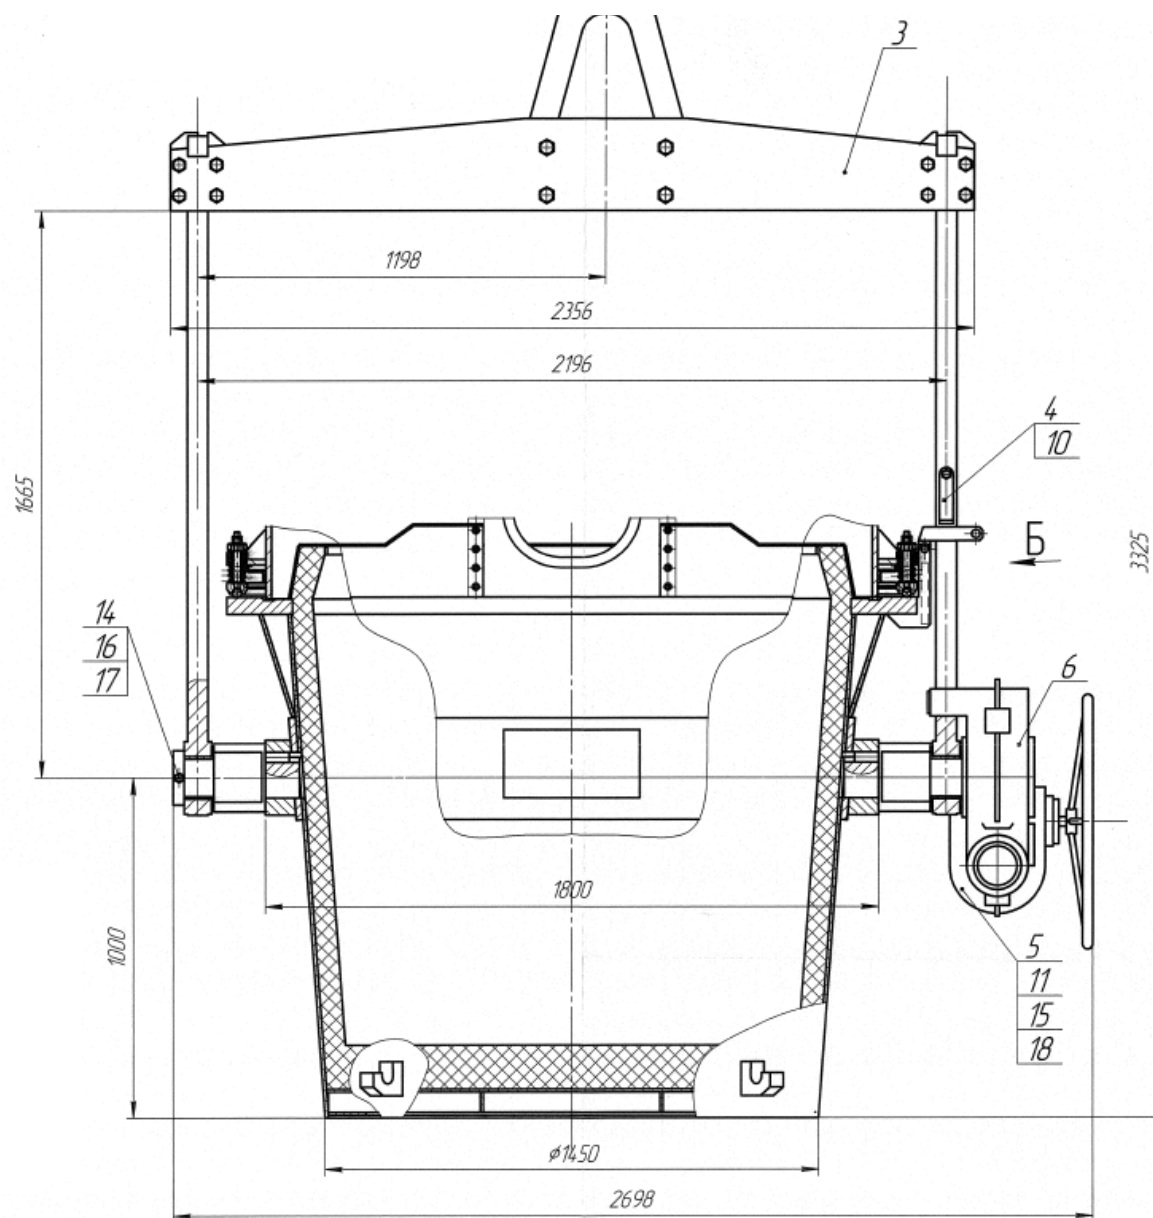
Транспортный ковш для алюминиевых расплавов
